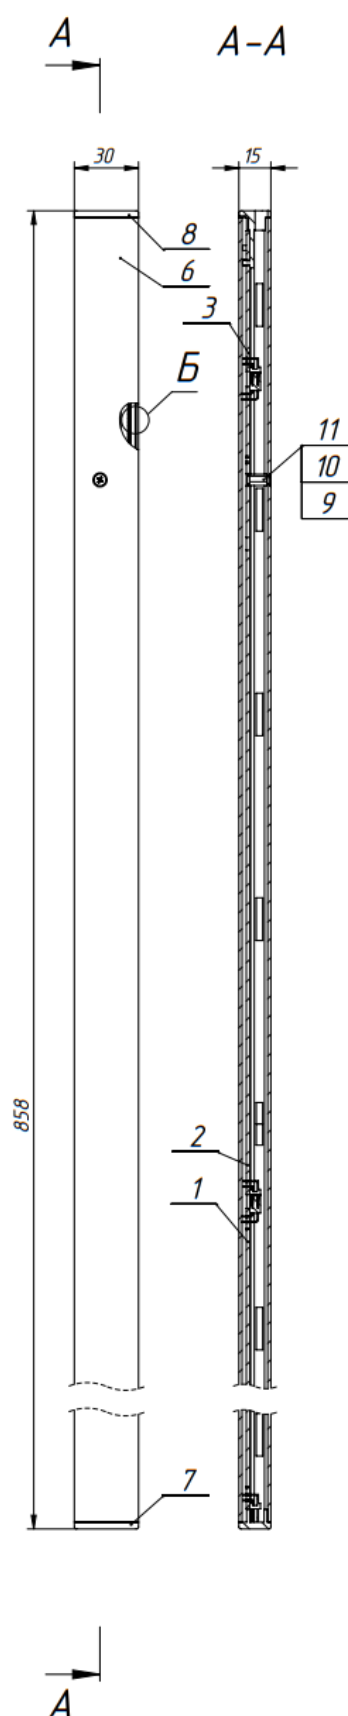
АРНИКА 1А. Сборочный чертеж
